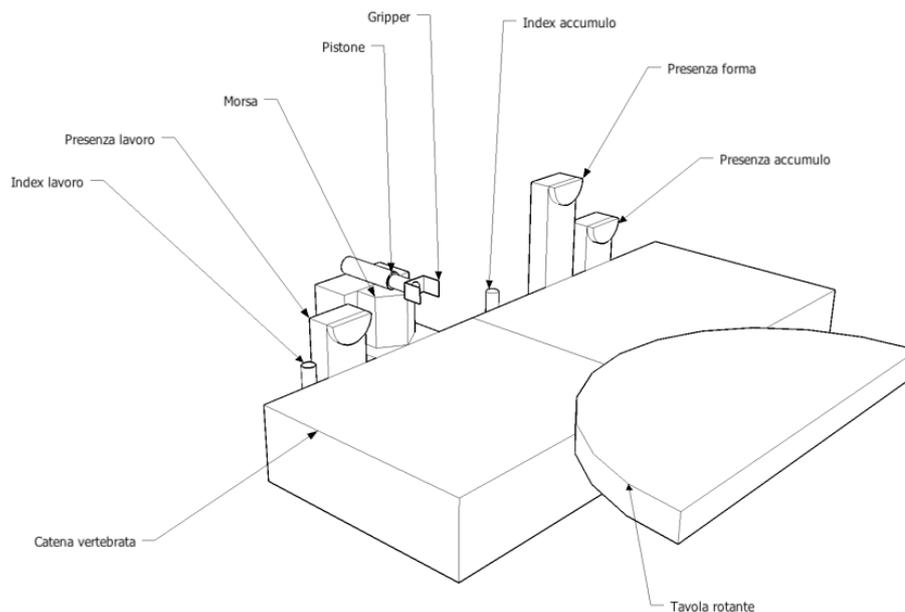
Schema della stazione d'interfaccia con il trasloelevatore
